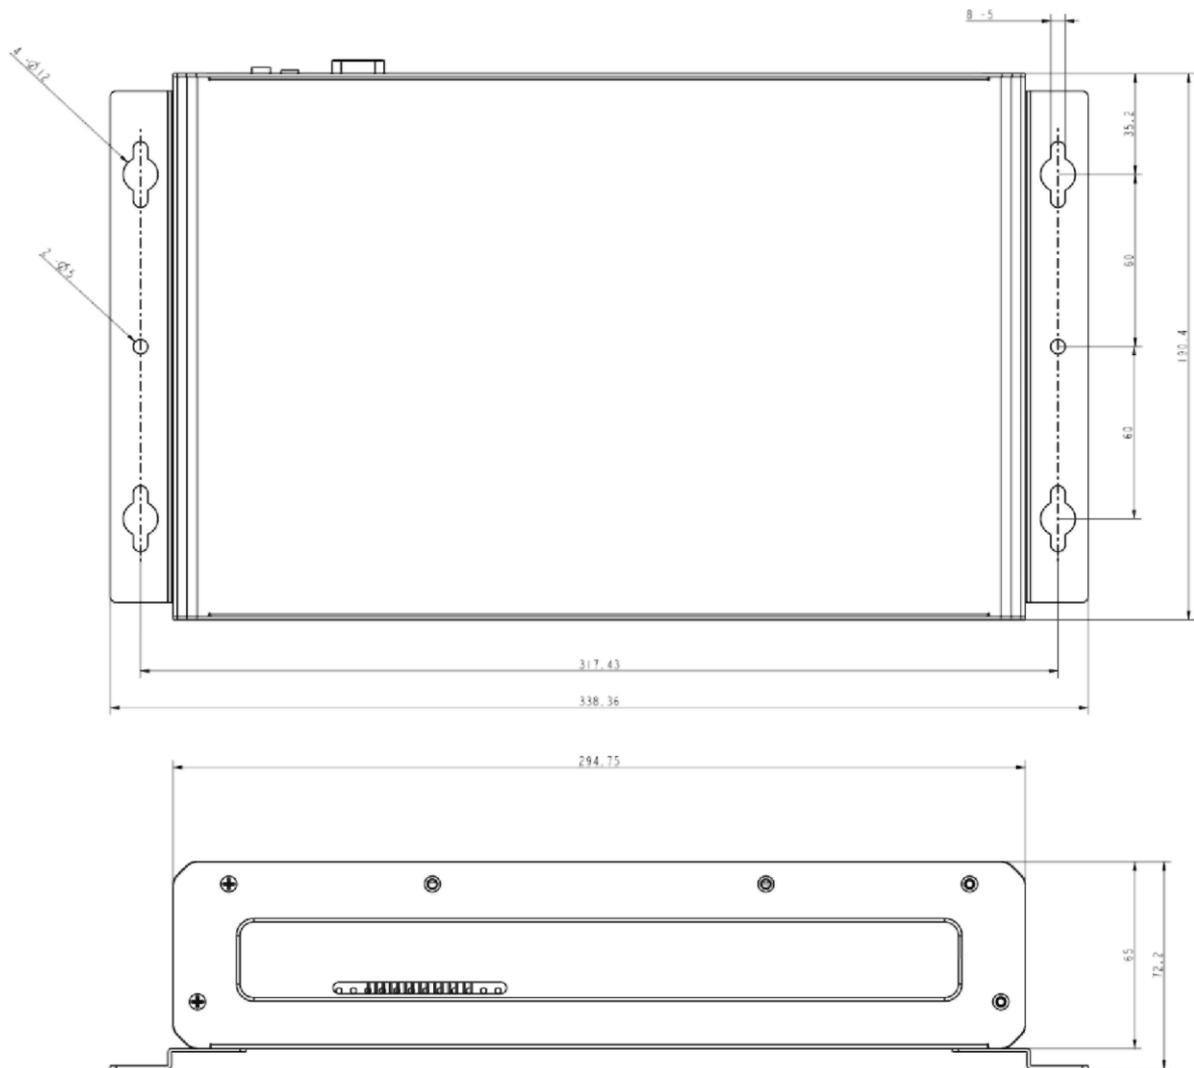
Габаритные размеры контроллера iVW-FH233
